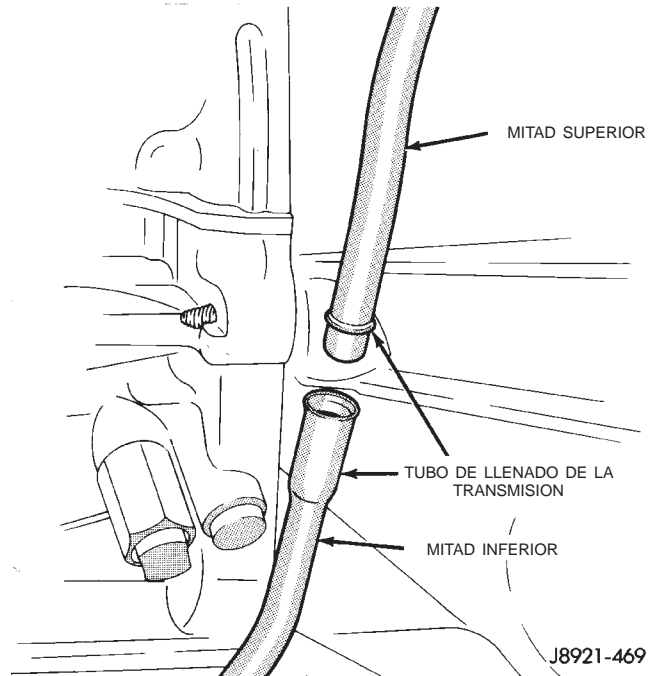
Tubo de llenado de la transmisión (de dos partes)
